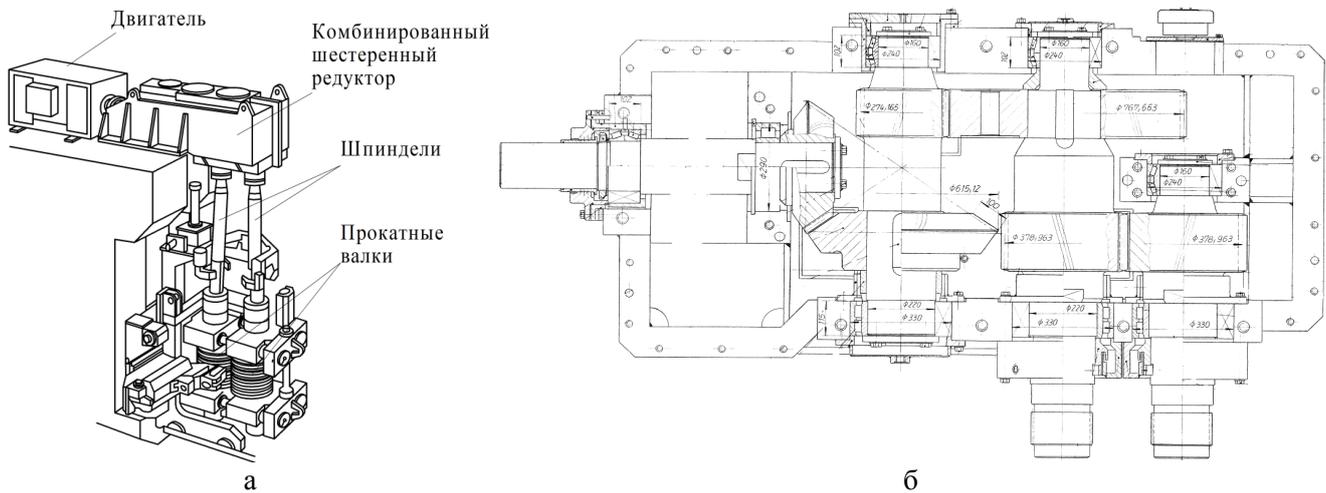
Общий вид (а) и разрез редуктора (б) комбинированного редуктора привода вертикальных валков
